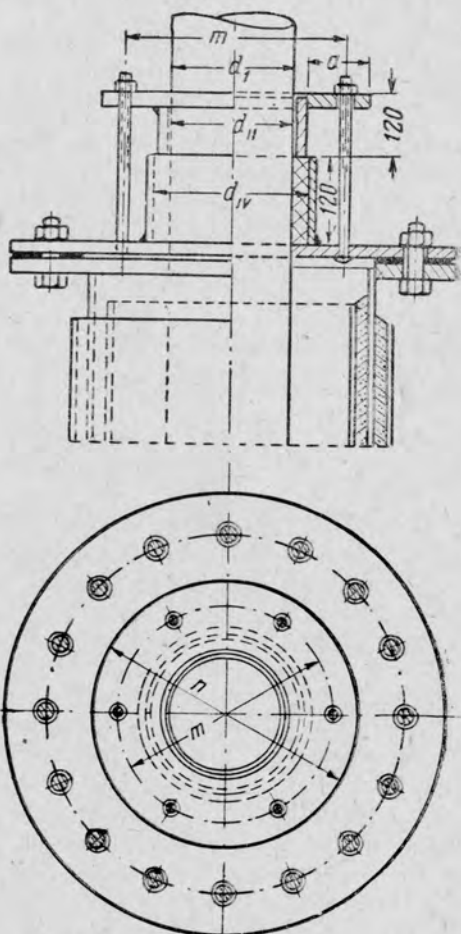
Железный сварной сальник для вертикального центробежного насоса.
